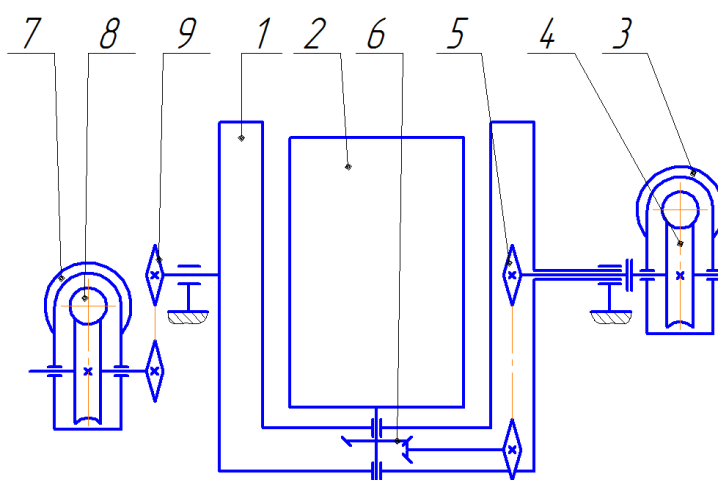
Кинематическая схема приводов: 1 – «рука», 2 – форма, 3 – электродвигатель, 4 - червячный редуктор, 5 – цепная передача, 6 – конический редуктор, 7 – электродвигатель, 8 - червячный редуктор, 9 – цепная передача
